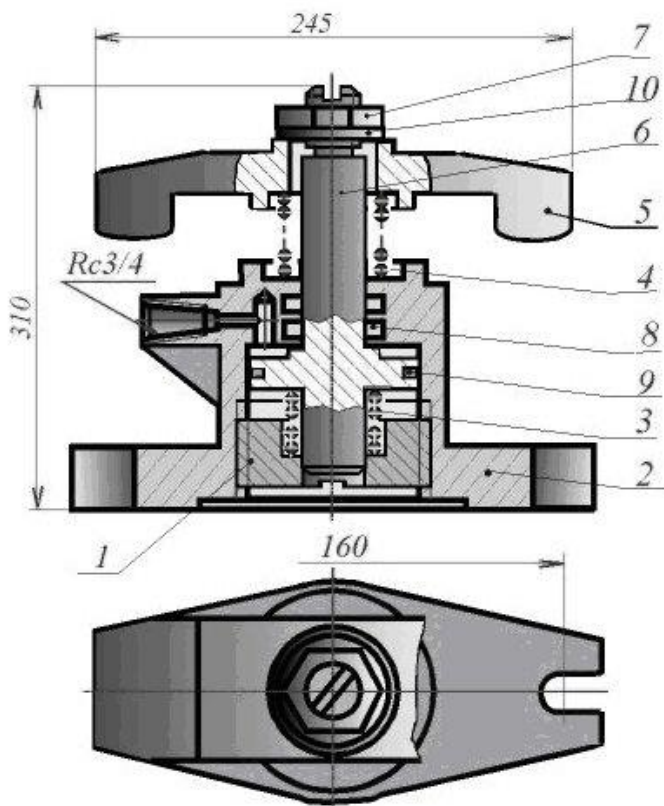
Прихват гидравлический (сборочный чертеж)
